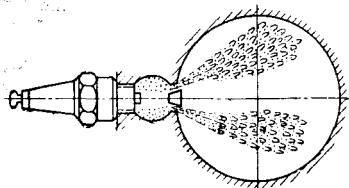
Схематическое устройство двигателя с форкамерно-факельным зажиганием
